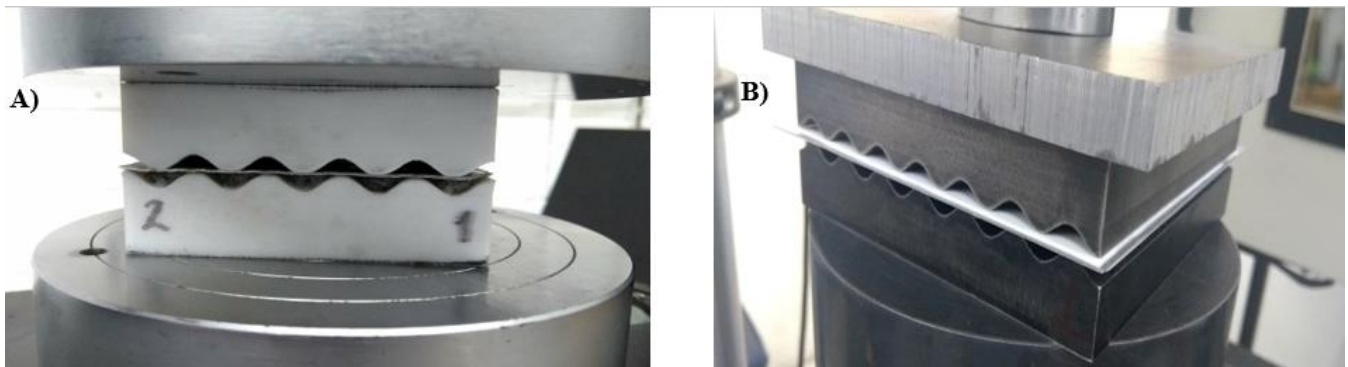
1. Inicio de proceso RCS. A) Molde de policarbonato y B) Molde de acero.
